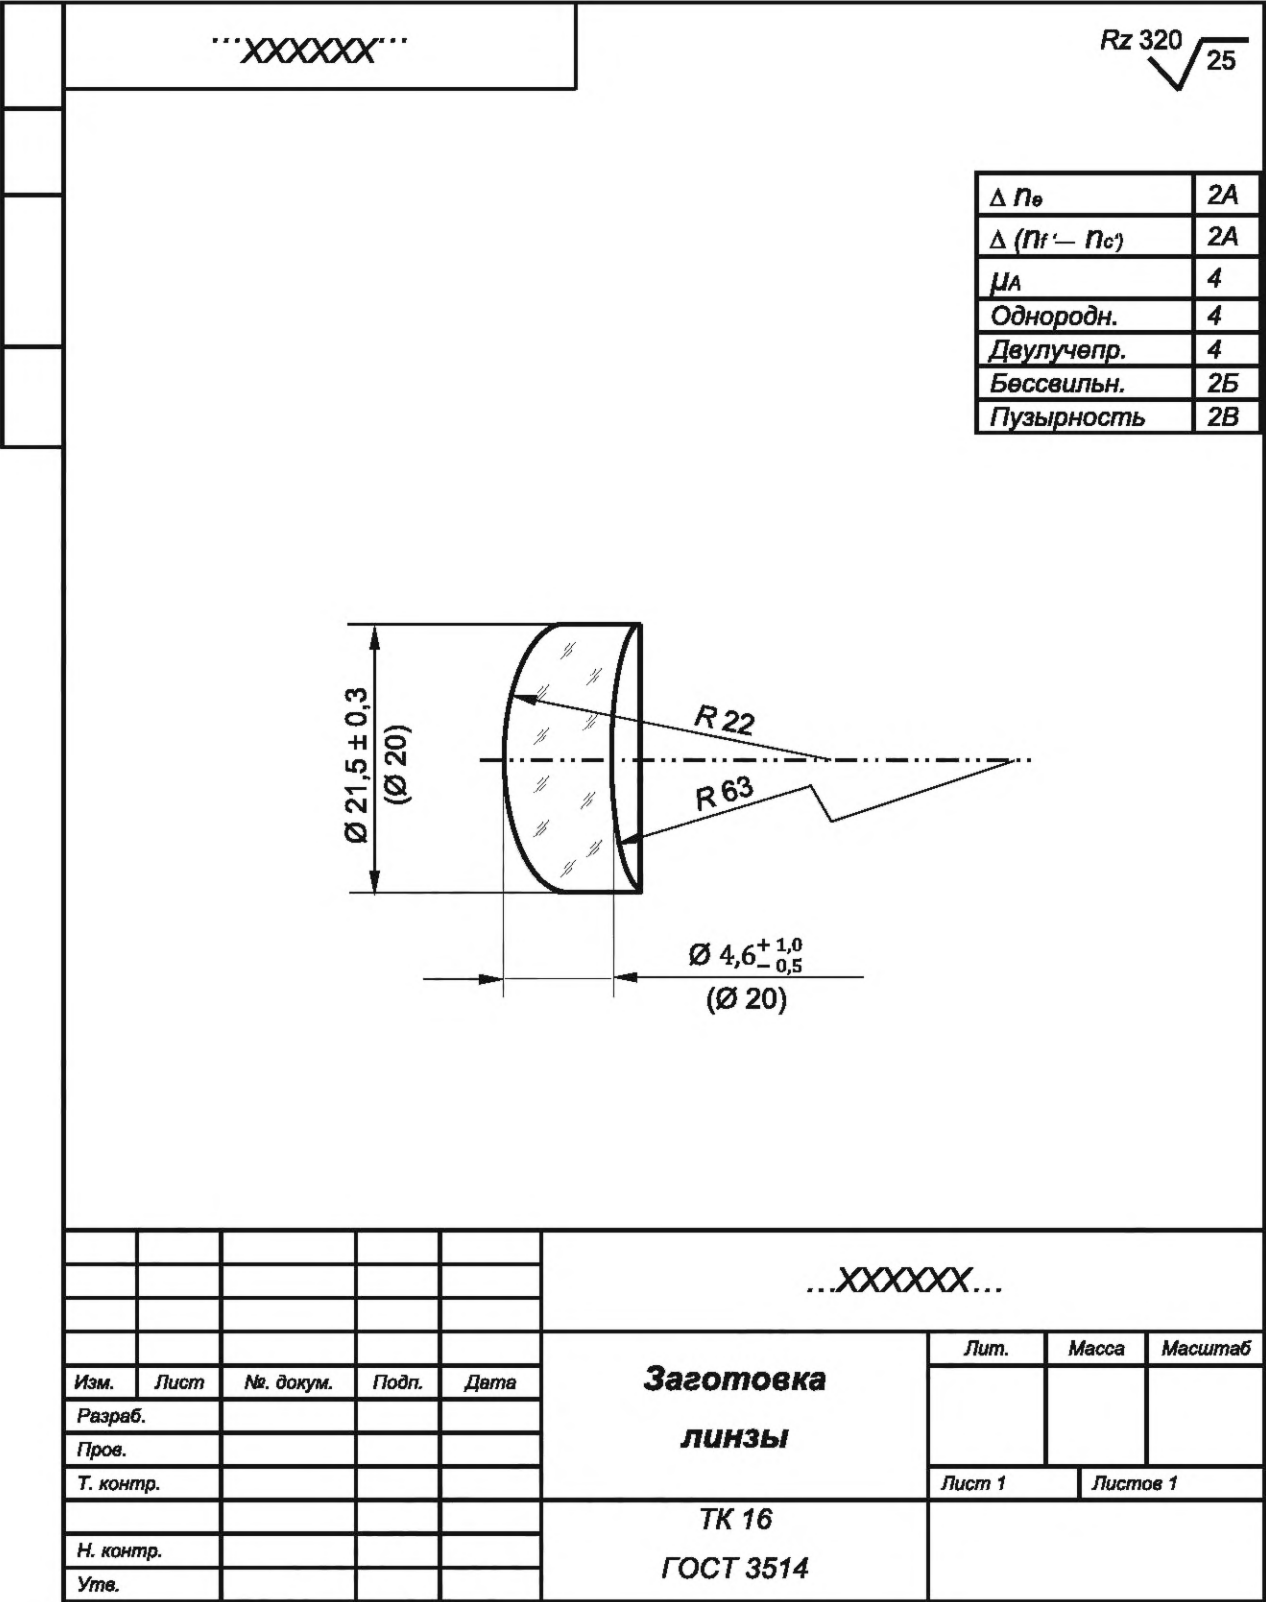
Чертеж заготовки линзы из стекла марки ТК 16 по ГОСТ 3514
